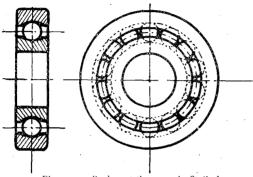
Roulement theorique de Stribeck (vue en coupe et de face.
